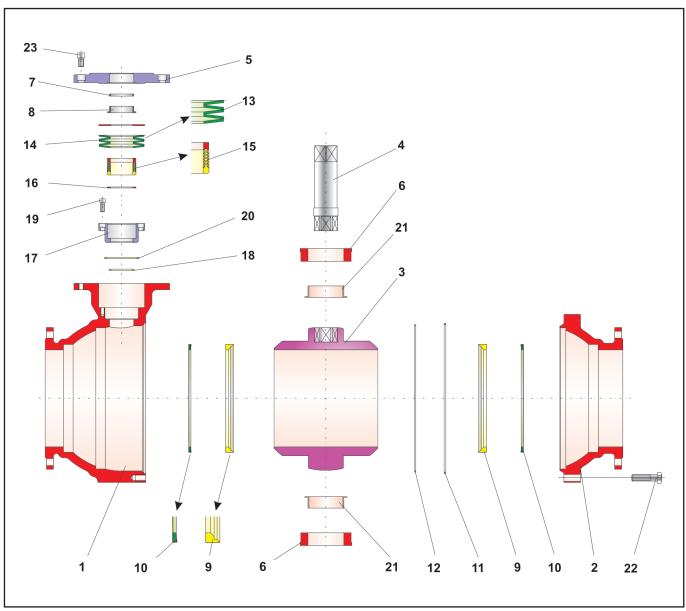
Despiece de la válvula de bola Tipo BR 26s
